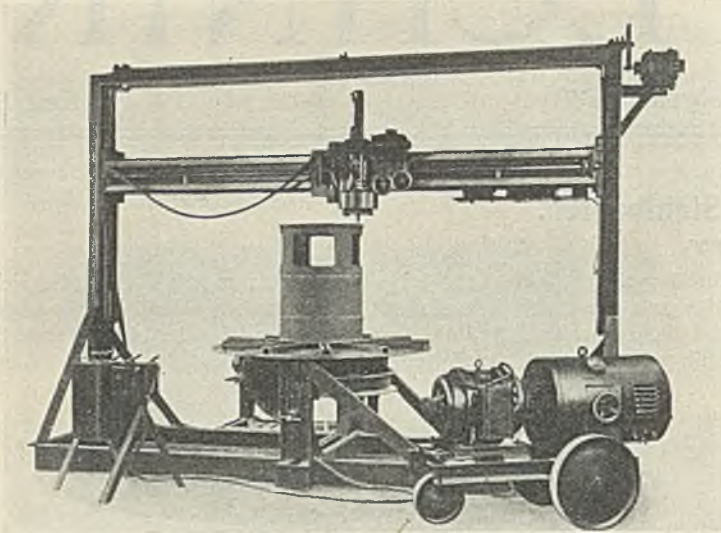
Schweißmaschine der AG. Elin.
